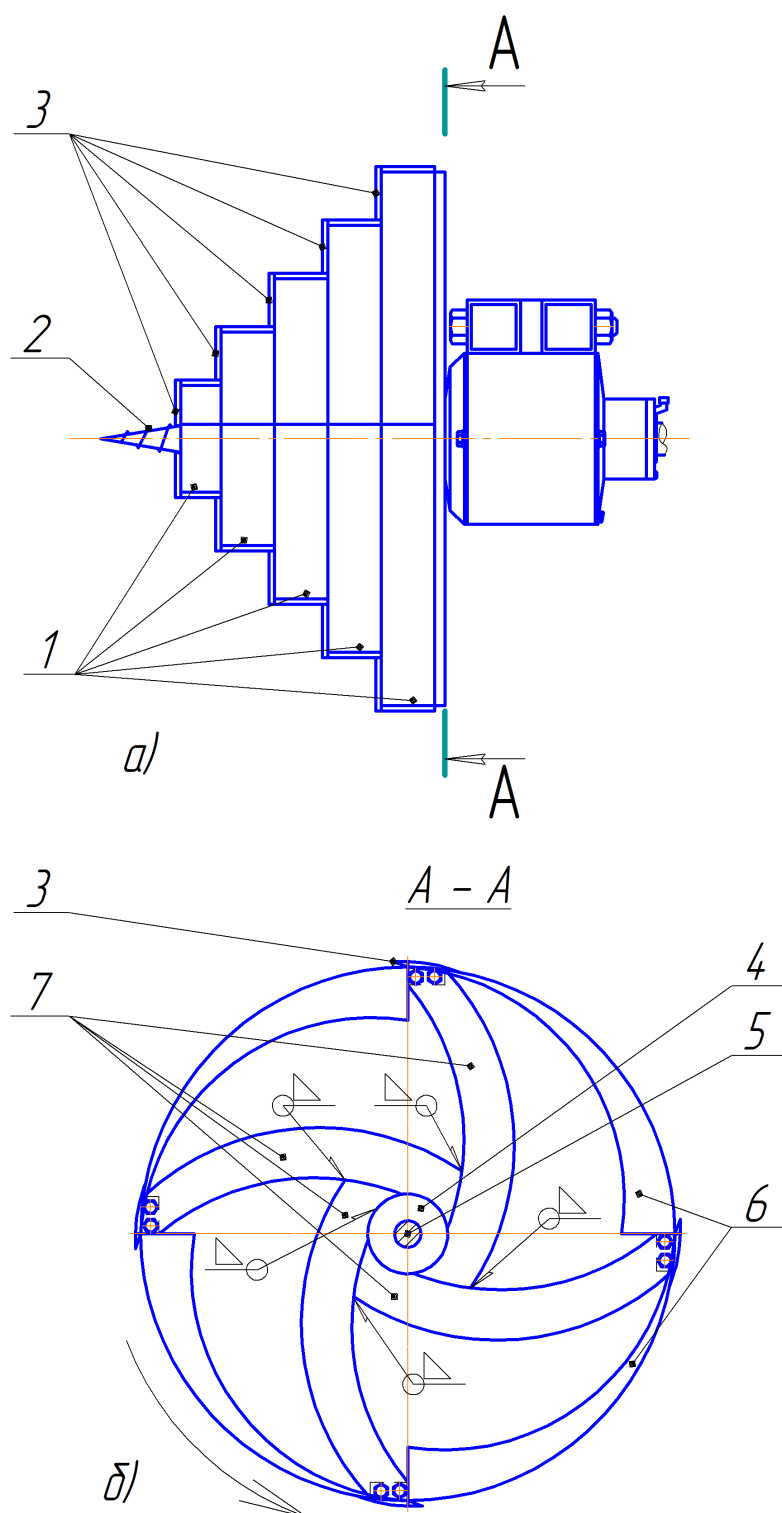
Прямоточный роторный рыхлитель: а – вид сбоку; б – разрез А – А; 1 – окружной нож; 2 – спиральный нож; 3 – торцевой нож; 4 – опорный диск; 5 – вал; 6 – лопасть; 7 – держатель
